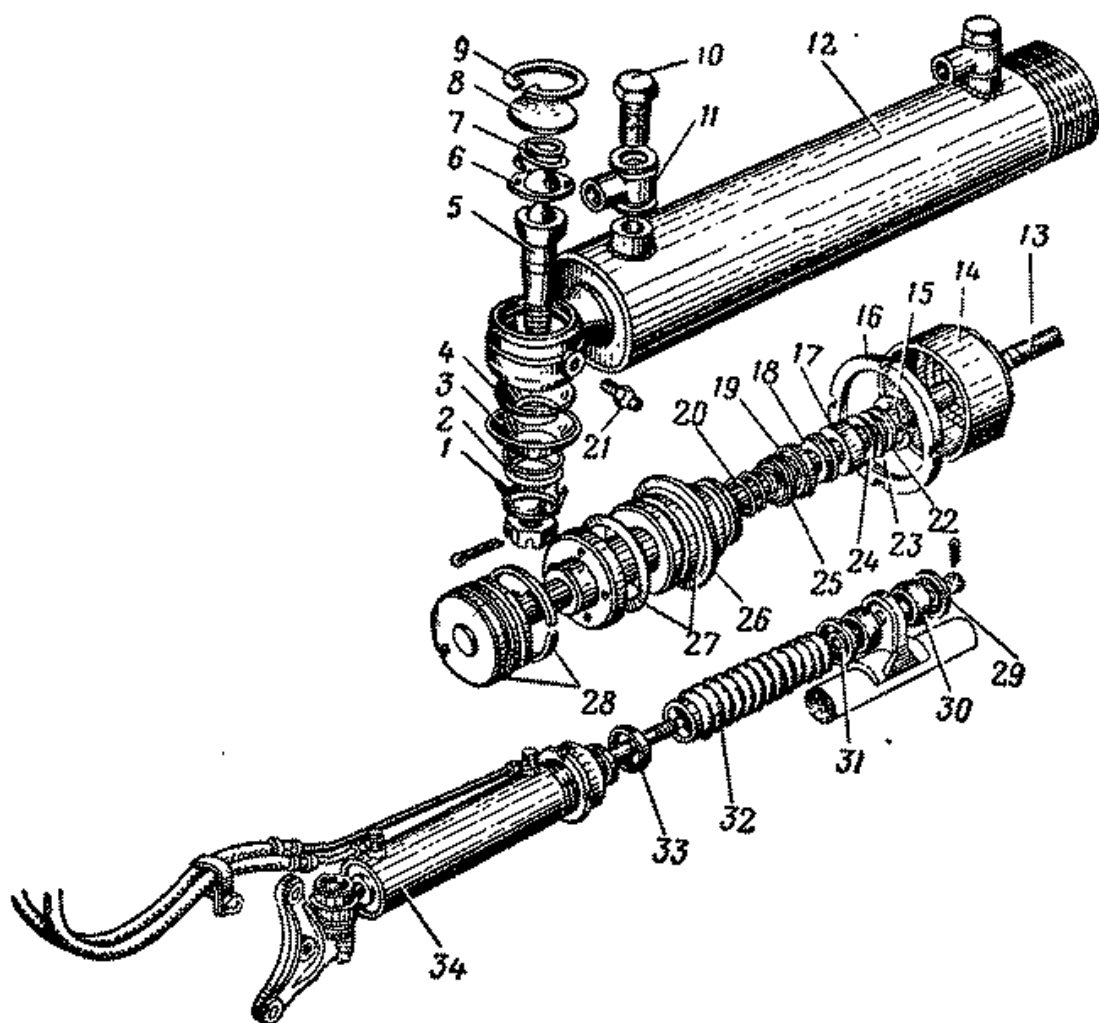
Детали силового цилиндра гидроусилителя руля:
